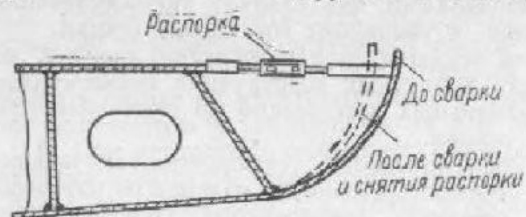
Обратный выгиб свободного участка обшивки с применением домкрата-распорки.
